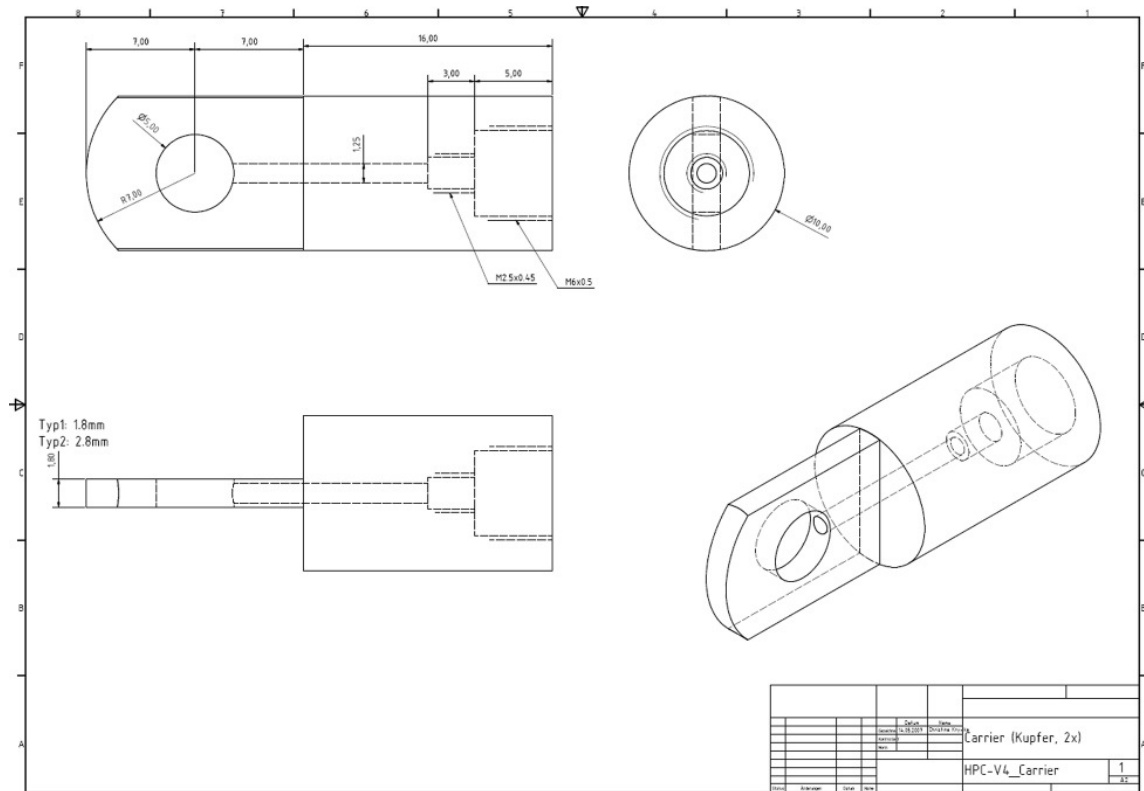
Technische Zeichnungen der Hochdruckzellenkomponenten
